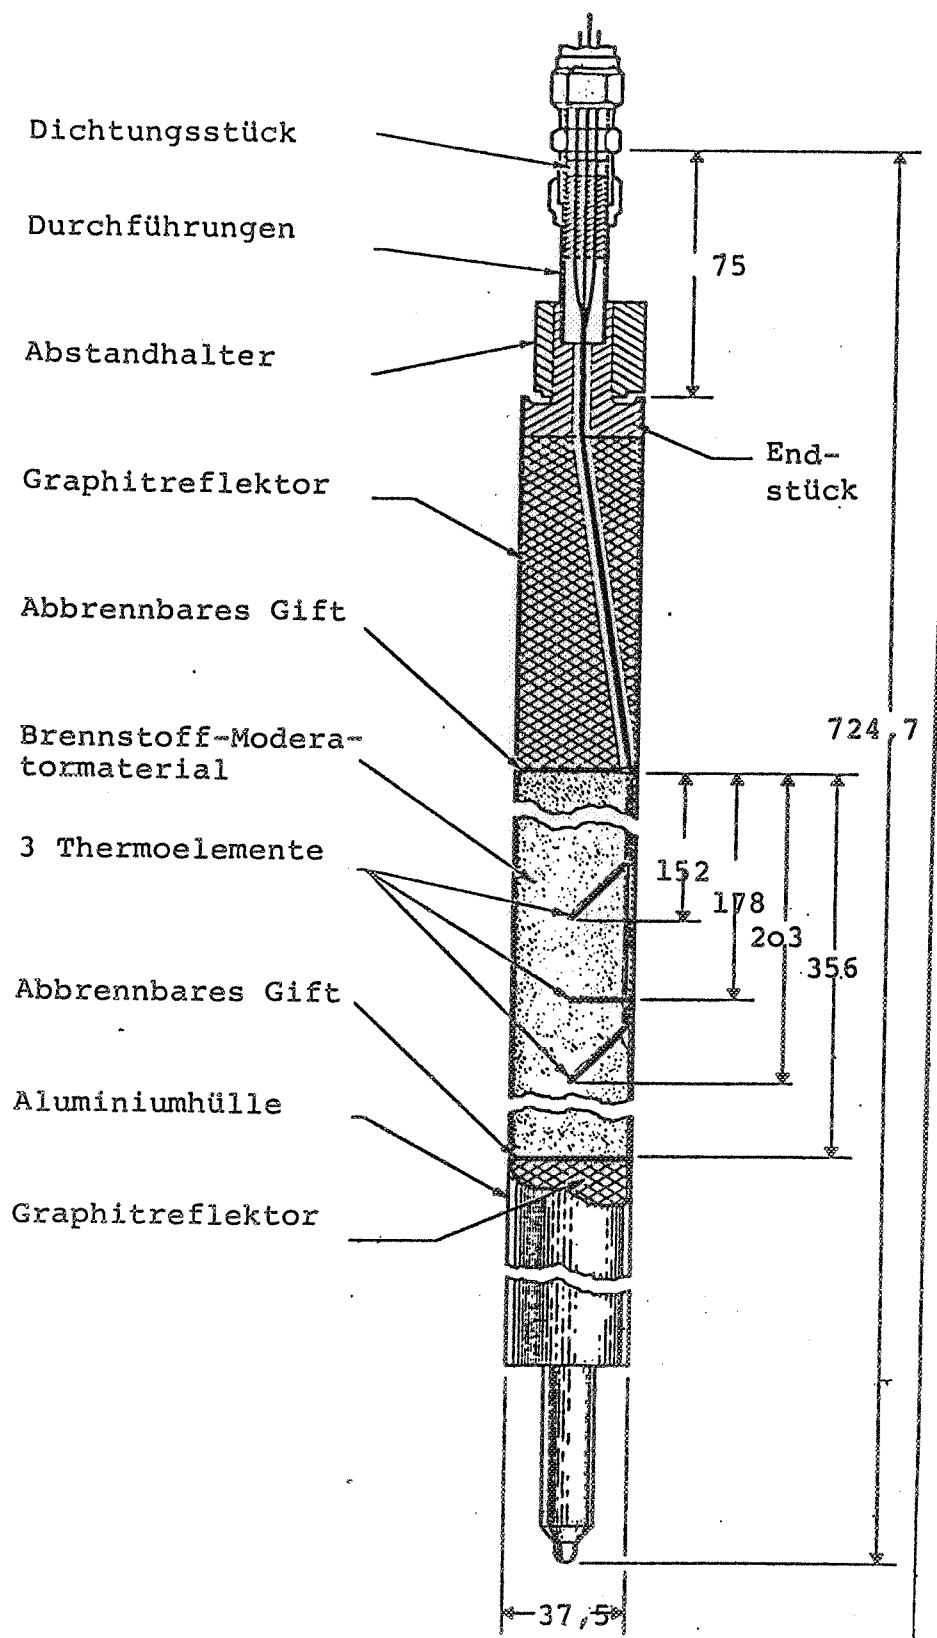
Instrumentiertes Brennelement (alle Angaben in mm)
